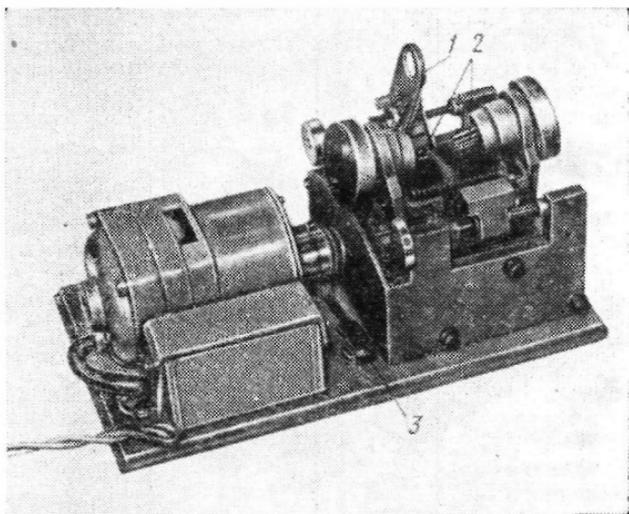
Полуавтоматический прибор для смазки часового механизма:
